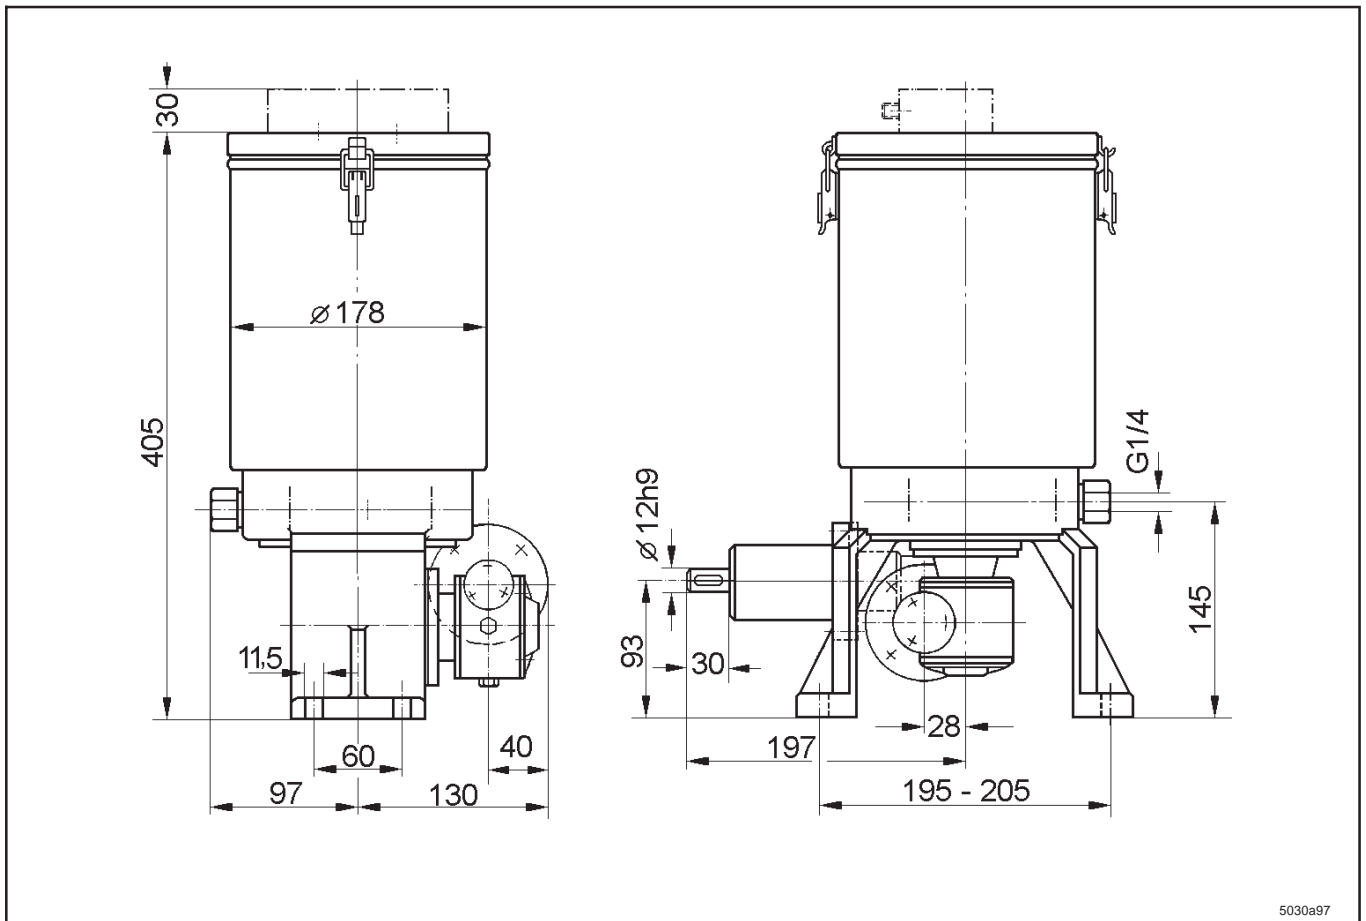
Maßzeichnung für Pumpe P205, 2-stufiges Getriebe, Blechbehälter, freies Wellenende
